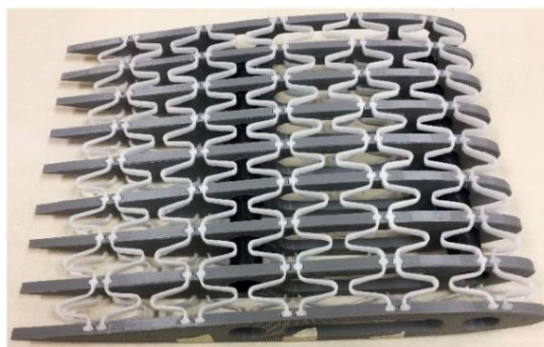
Крыло БПЛА, изготовленное с помощью FDM 3D-печати [16]
